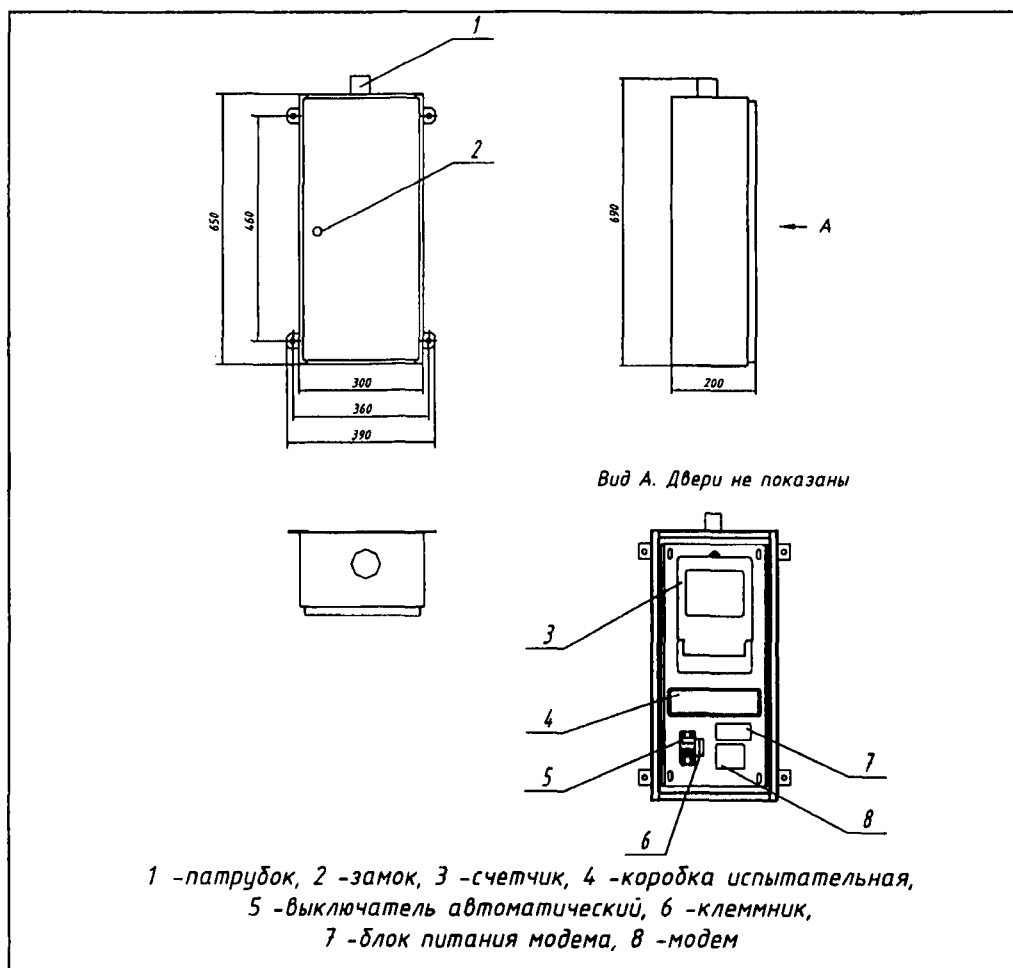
Габаритные и присоединительные размеры низковольтного модуля (шкафа учета)
